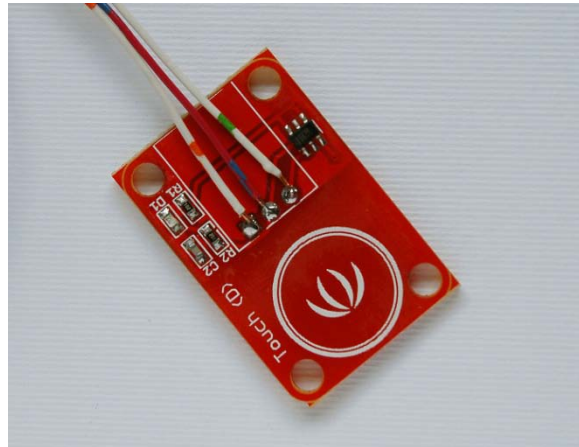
Reverso del sensor de toque. Los alambres soldados a la placa del sensor sustituyen al conector original.
